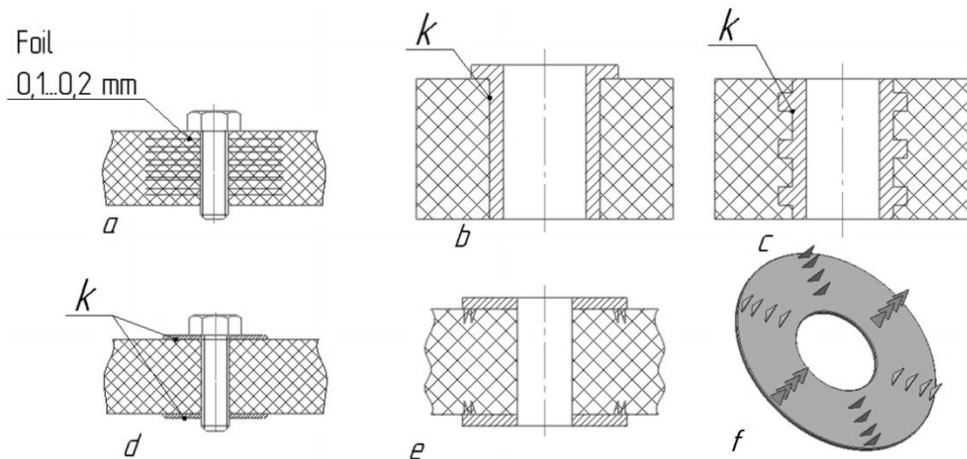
Усиления зоны соединения. (а) фольгирование; (b) установка промежуточных втулок; (c) (d) втулка с резьбовой внешней поверхностью; (e), (f) трансверсальные микроэлементы [3].
